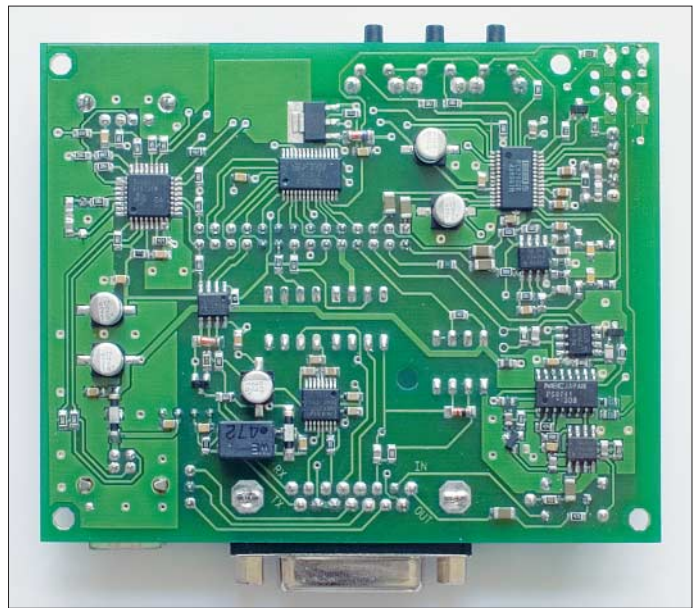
Fertig bestückte Platine; deutlich sind die Jumper auf dem Erweiterungsport zu erkennen.
